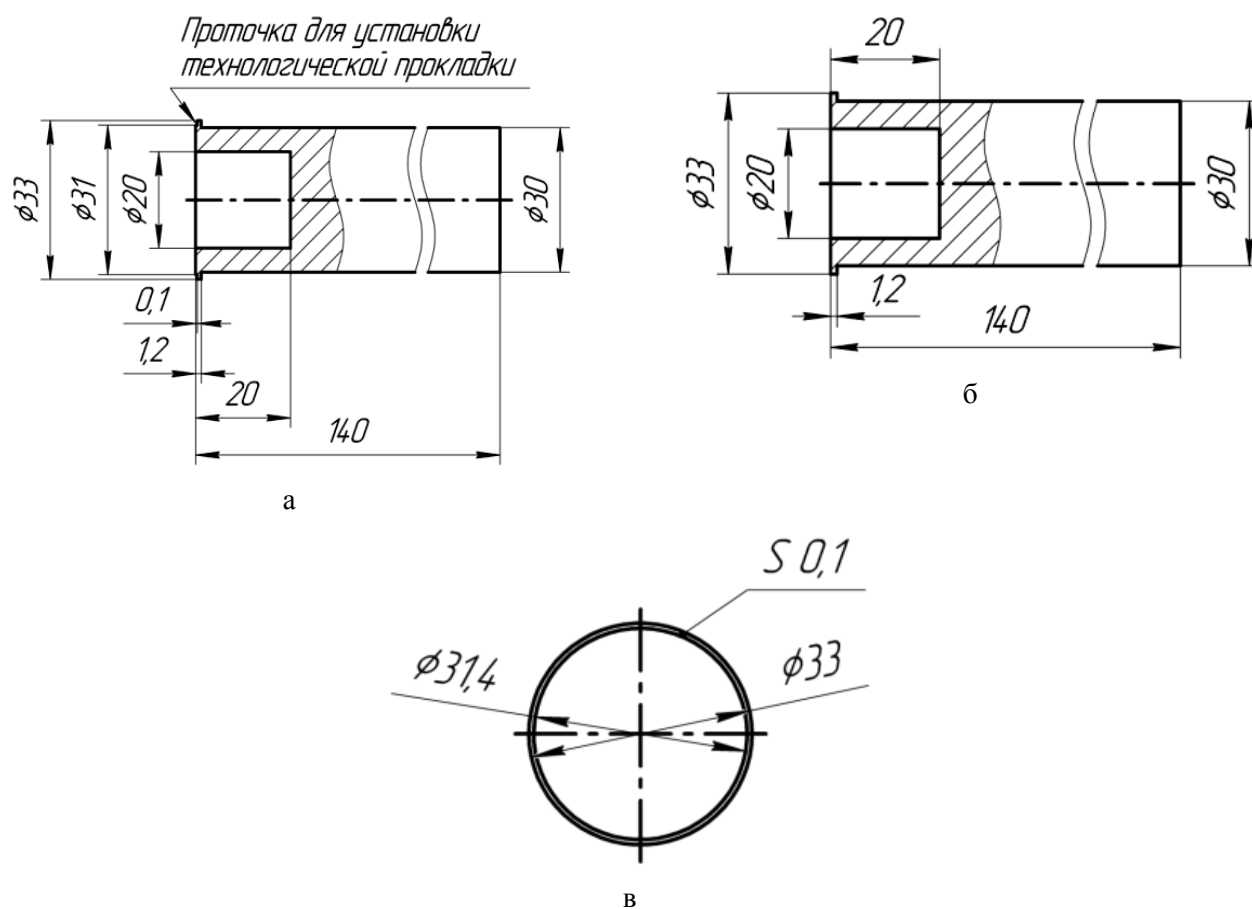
Конструкции деталей для изготовления образцов: а – с проточкой для установки технологической прокладки из сплава Х20Н80; б – без проточки; в – технологическая прокладка из сплава Х20Н80
